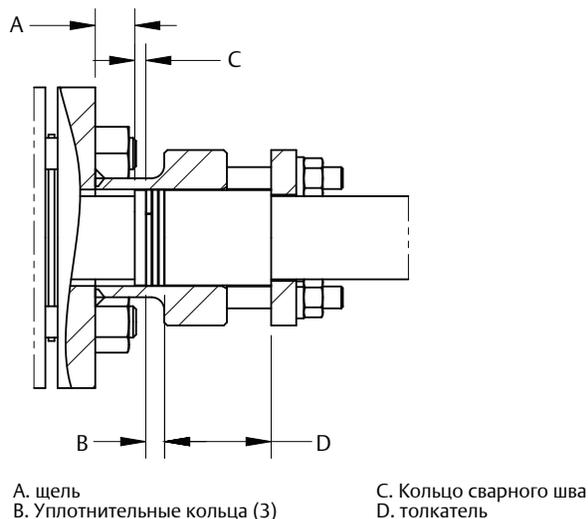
иллюстрирует вид сенсор Annubar Flange-Lok по завершении установки. Пожалуйста, обратите внимание, что между корпусом Pak-Lok и сварным кольцом должен быть зазор.
